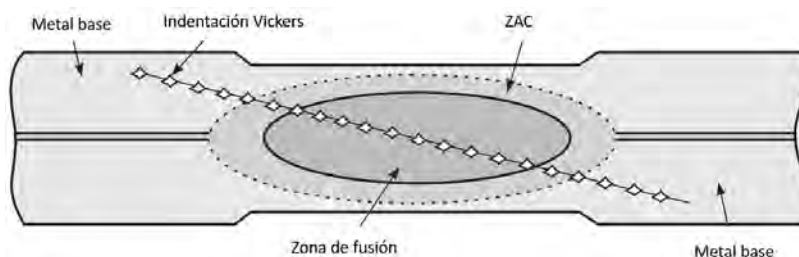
Esquema de dureza en soldadura RSW [11]
